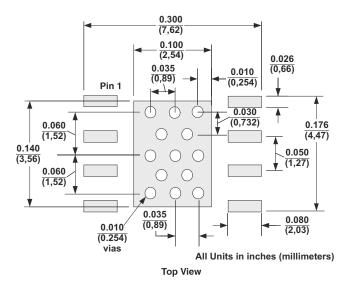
DDA PowerPAD PCB Etch and Via Pattern
